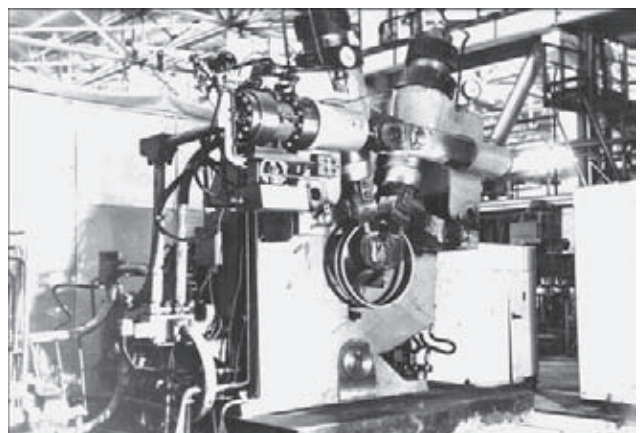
Кольцевая заготовка в зажимных устройствах стыкосварочной машины K607
